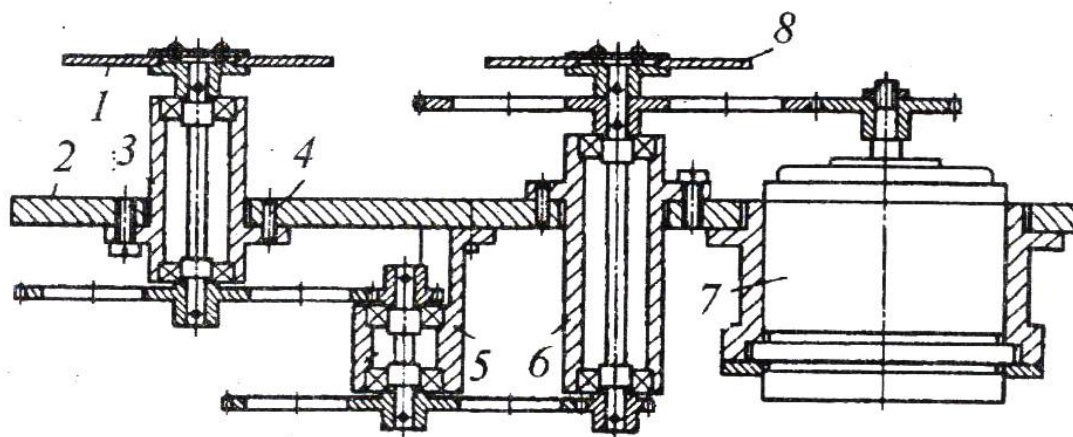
Одноплатный корпус с двухопорным креплением валов
